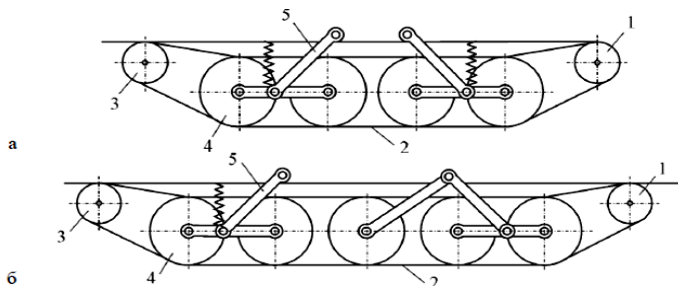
Схема подвески гусеничного трелевочного трактора: а – упругая рычажно-баланси́рная подвеска; б – полужесткая рычажно-баланси́рная подвеска: 1 – ведущее колесо (звездочка); 2 – гусеничная цепь; 3 – направляющее колесо; 4 – опорные катки; 5 – рычаги подвески
